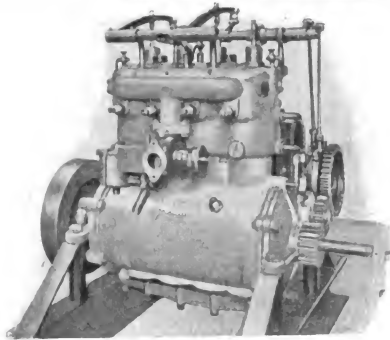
Vierzylindermotor von Maurer (Nürnberg). Zylinder, Kurbelgehäuse und Rohrleitungen zusammen aus einem Stück gegossen.
